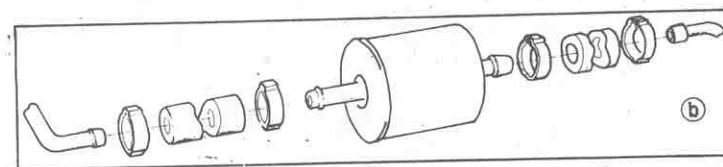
, detalle b.- Montaje del filtro de nafta entre la bomba y el carburador.
